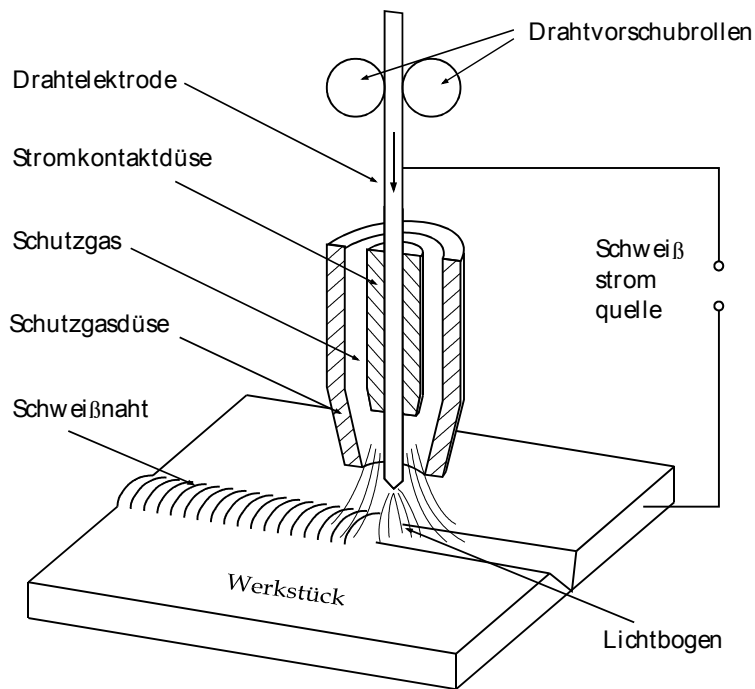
Schematische Darstellung des Schutzgasschweißens. Zwischen der Drahtelektrode und dem Werkstück fließt ein Strom, der ein Plasma im Schutzgas erzeugt, das durch die Düse über die Elektrode strömt und gleichzeitig das Schmelzbad auf dem Werkstück vor Reaktionen mit der Luft schützt
